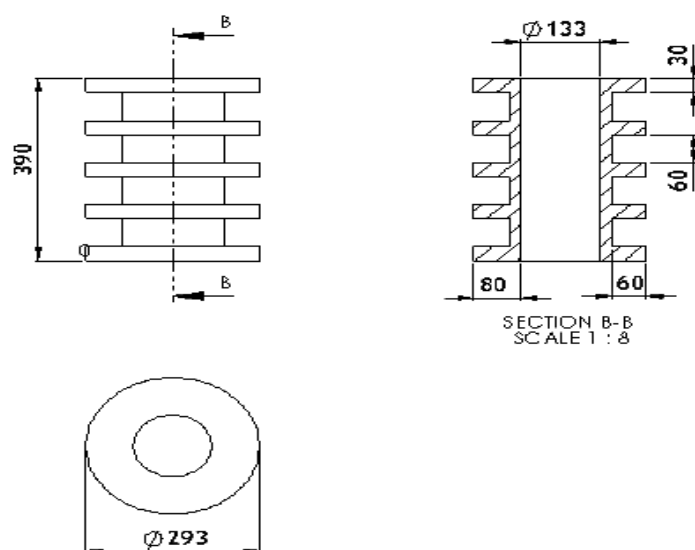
Dimensões finais do secundário (mm) do gerador linear tubular [21]
